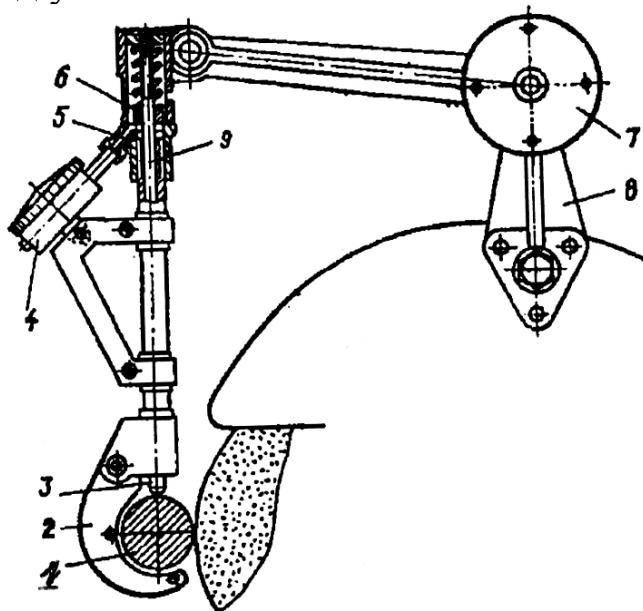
Пристрій для автоматичного контролю розміру шийки вала під час шліфування:
